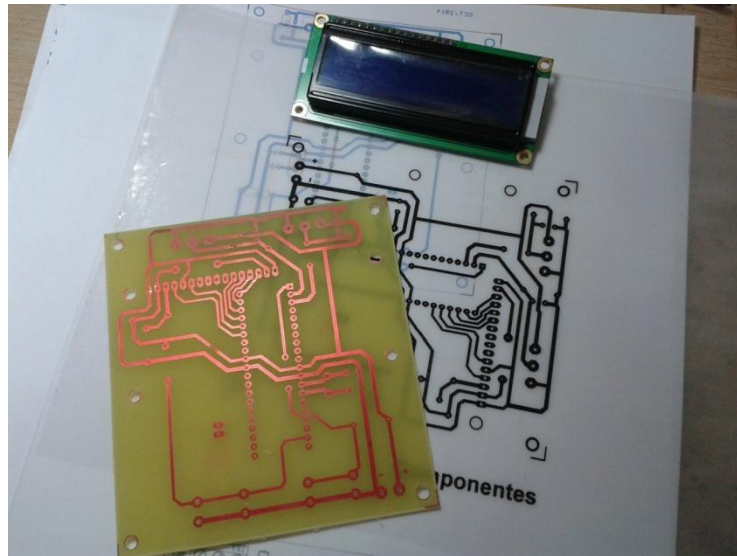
DISEÑO E IMPRESIÓN DEL PCB.
